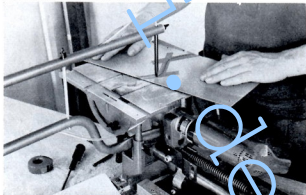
Sägen von Holzbohlen für einen Flugmodellrumpf. Gearbeitet wird mit einem Laubsägeblatt für Holz.
